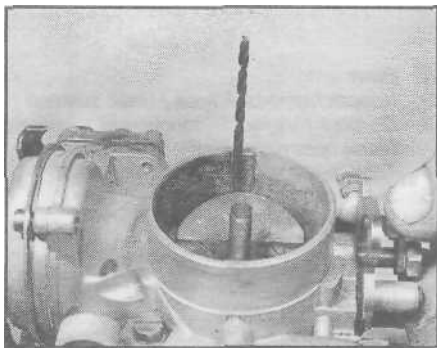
, а. Проверка зазора воздушной заслонки при помощи сверла
